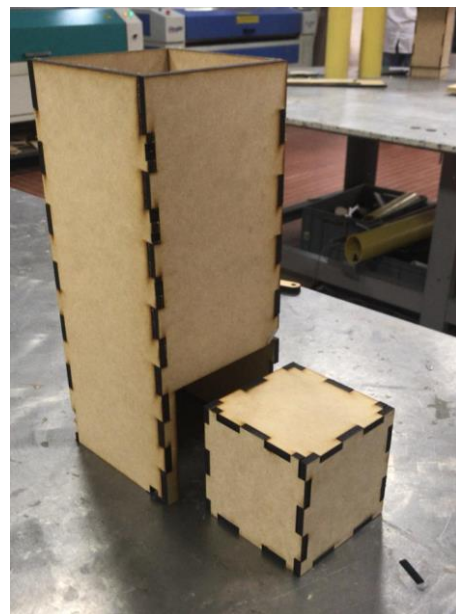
Dispositivo almacenador de cajas previo a la estampación.
